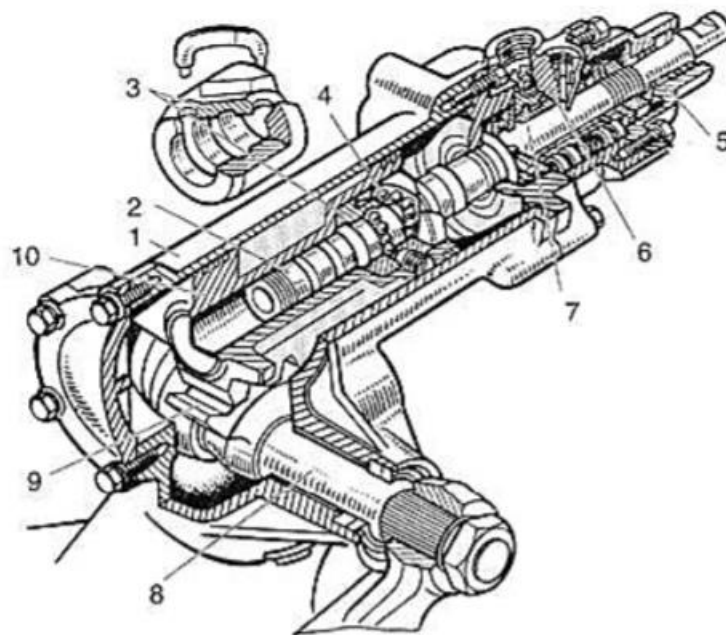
Будова рульового механізму з вбудованим гідропідсилювачем: 1 - картер; 2 – гвинт; 3 – гайка; 4 – кульки; 5 – рульовий вал; 6 – корпус клапана; 7 – золотник; 8 – вал сошки; 9 – зубчатий сектор; 10 – поршень-рейка [3]
